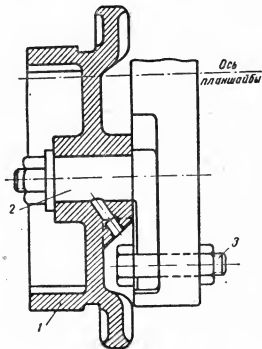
Схема установки на планшайбе токарного станка храповой муфты автомата:
